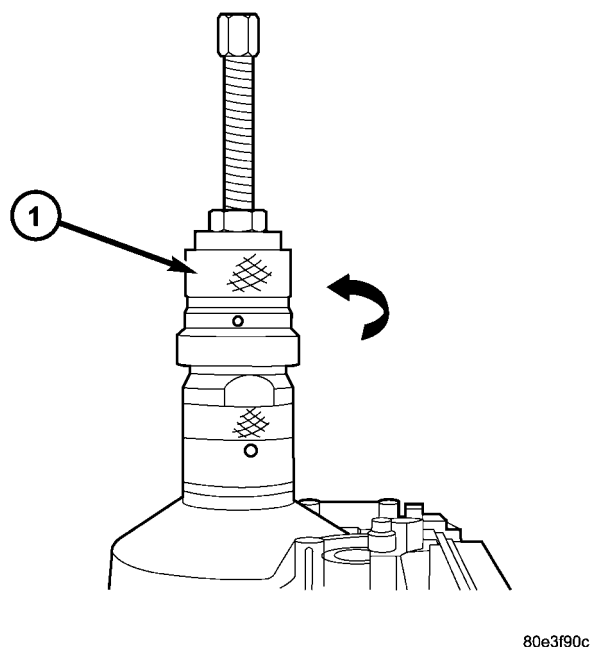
Montaje de la herramienta especial para retirar el cojinete trasero del eje de salida
